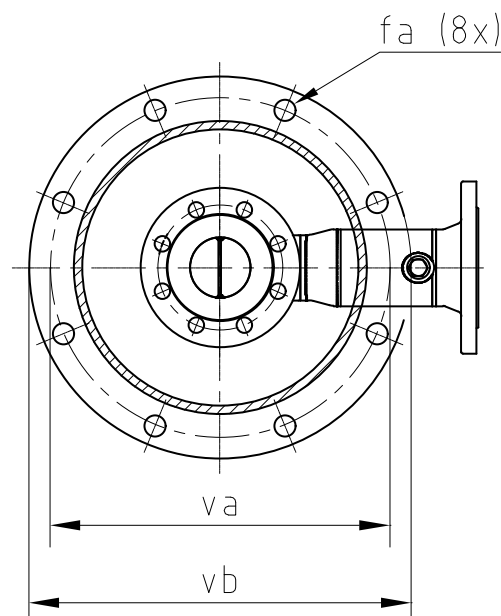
Размеры подкладок под стойки (вид сверху).
